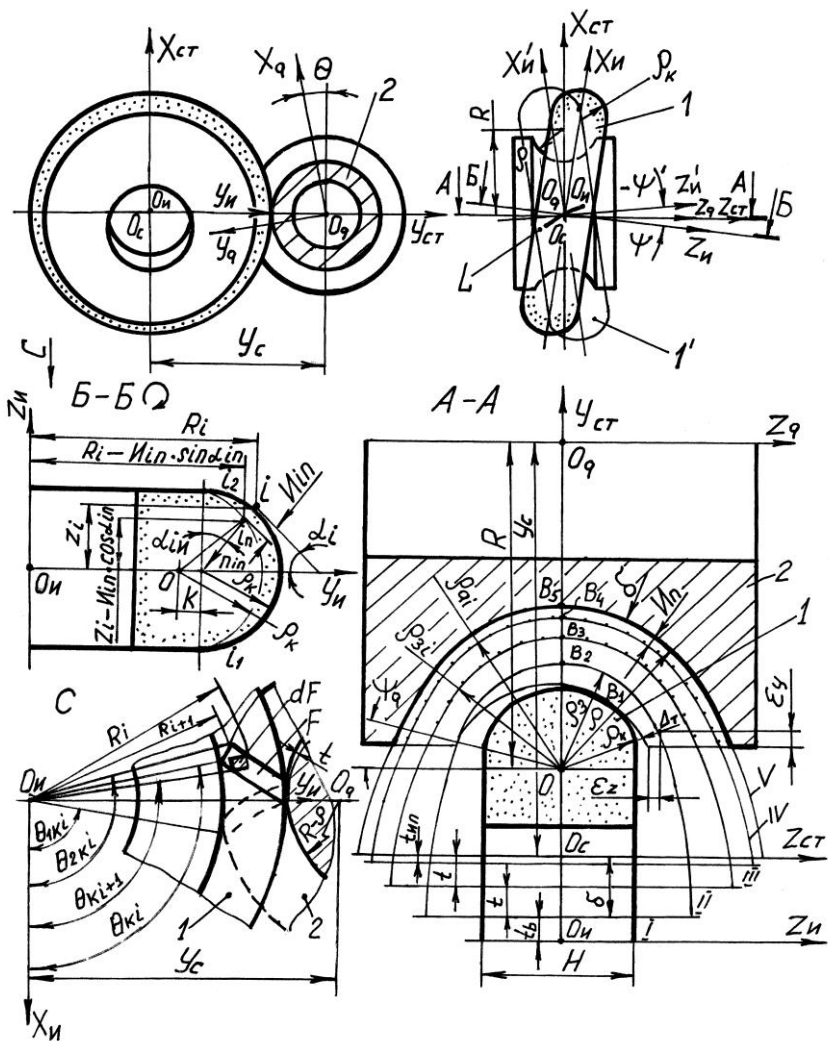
Схема шлифования торцовых поверхностей с управляемым углом скрещивания осей круга и детали
